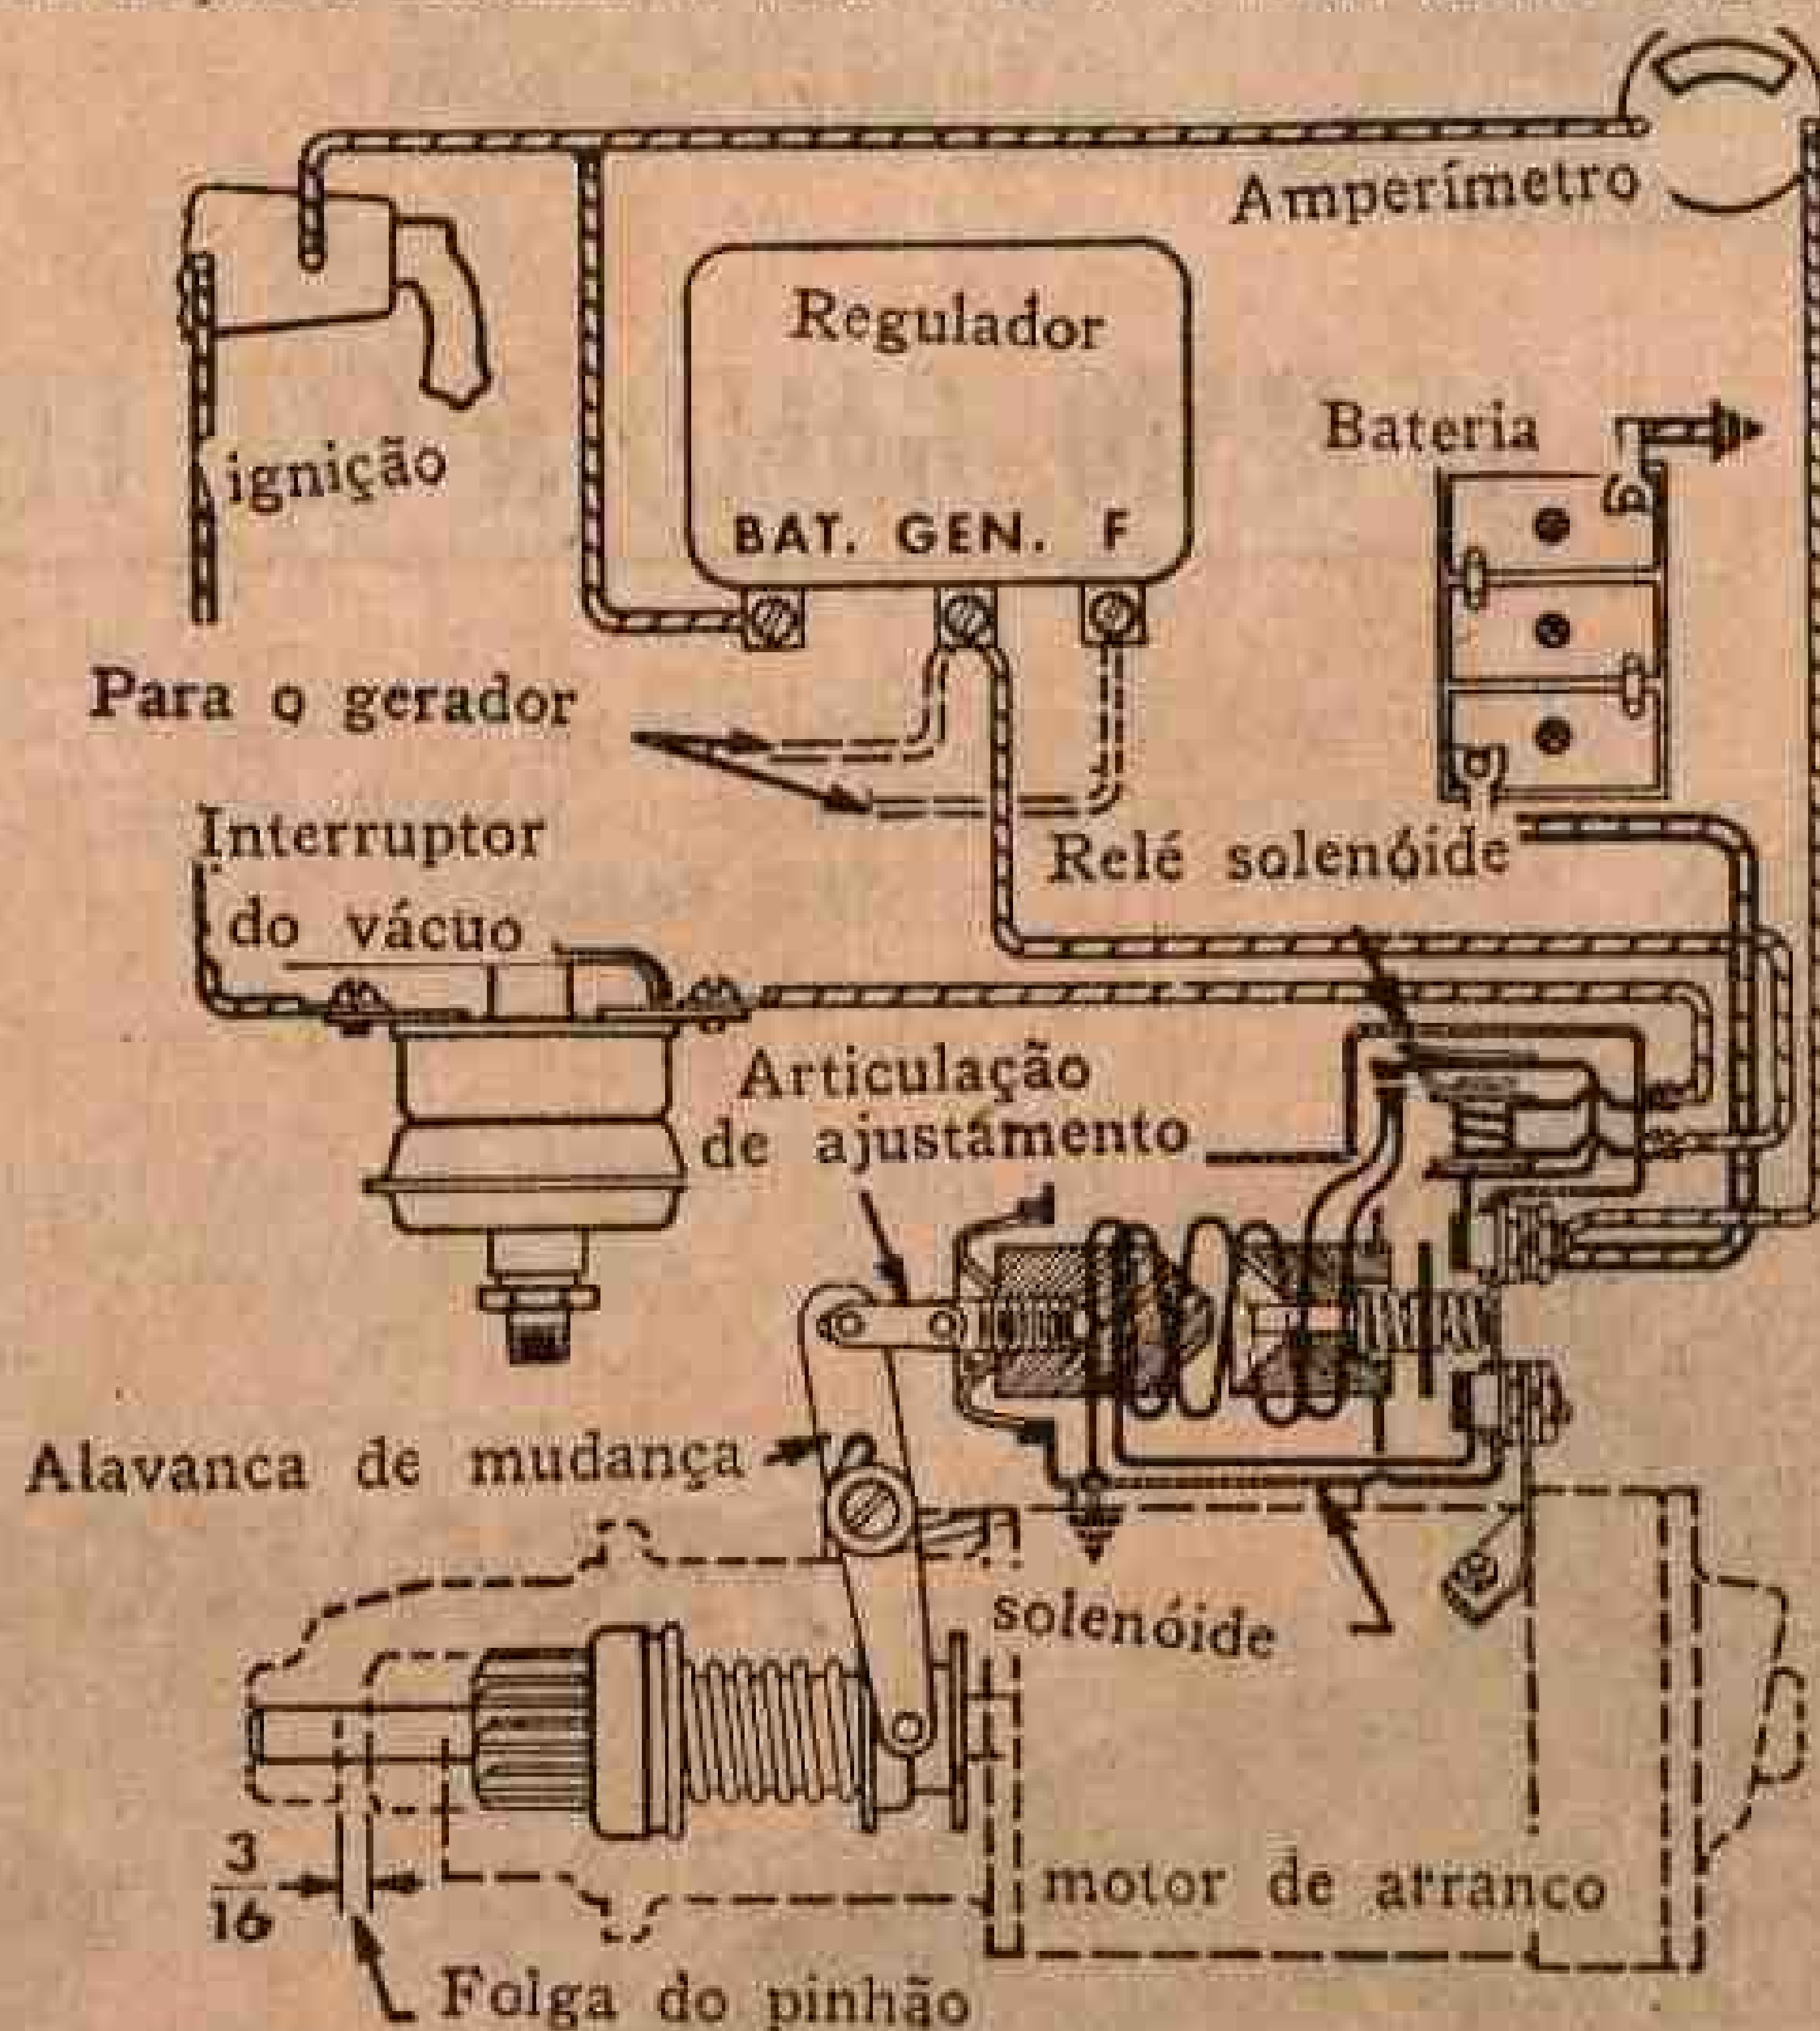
Solenóide e circuito de controle do motor de arranco.
